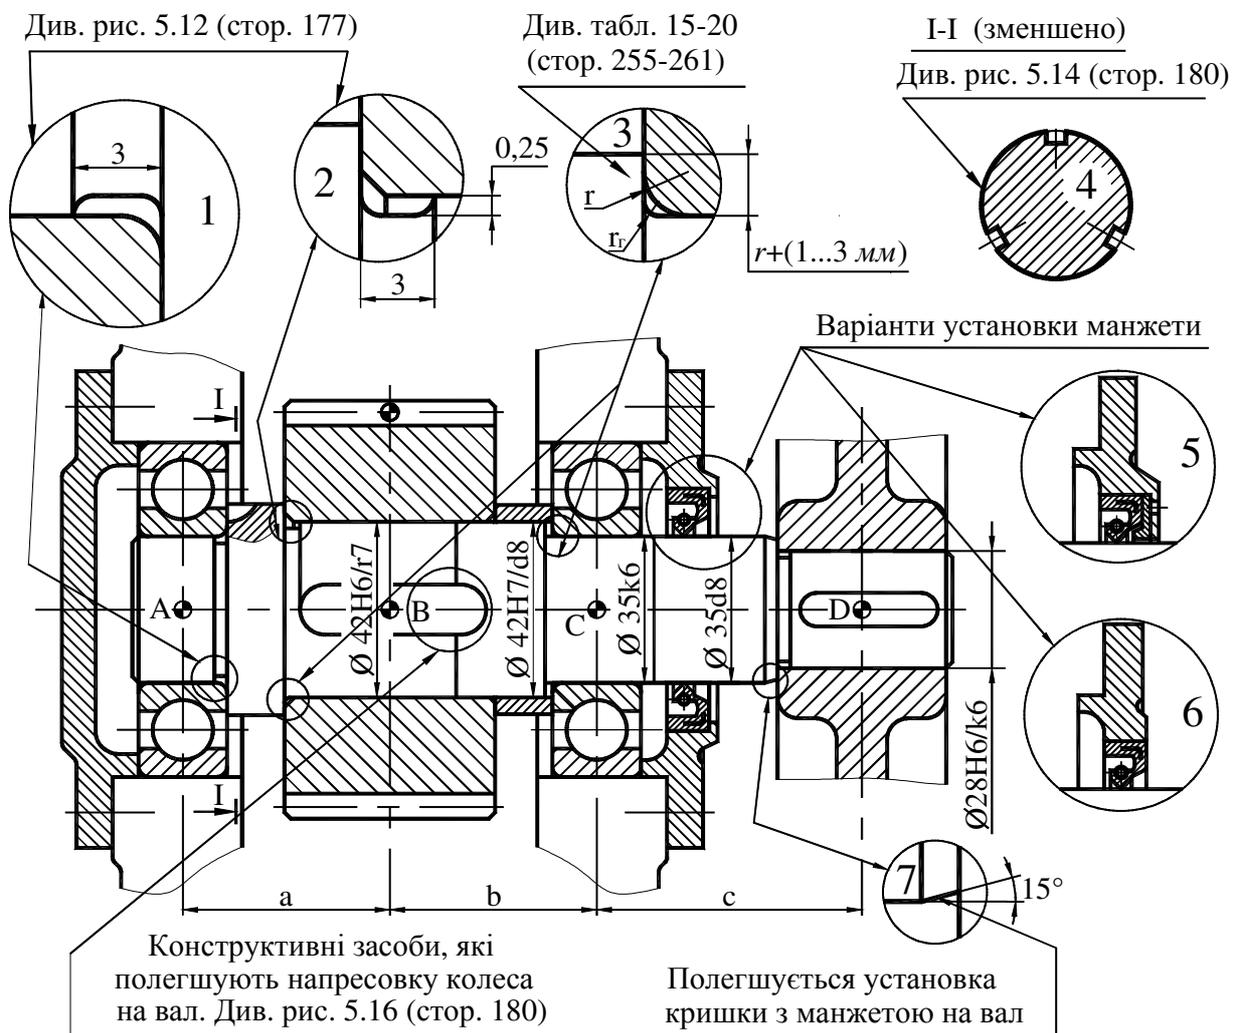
Приклад конструкції вхідного вала одноступеневого циліндричного редуктора
